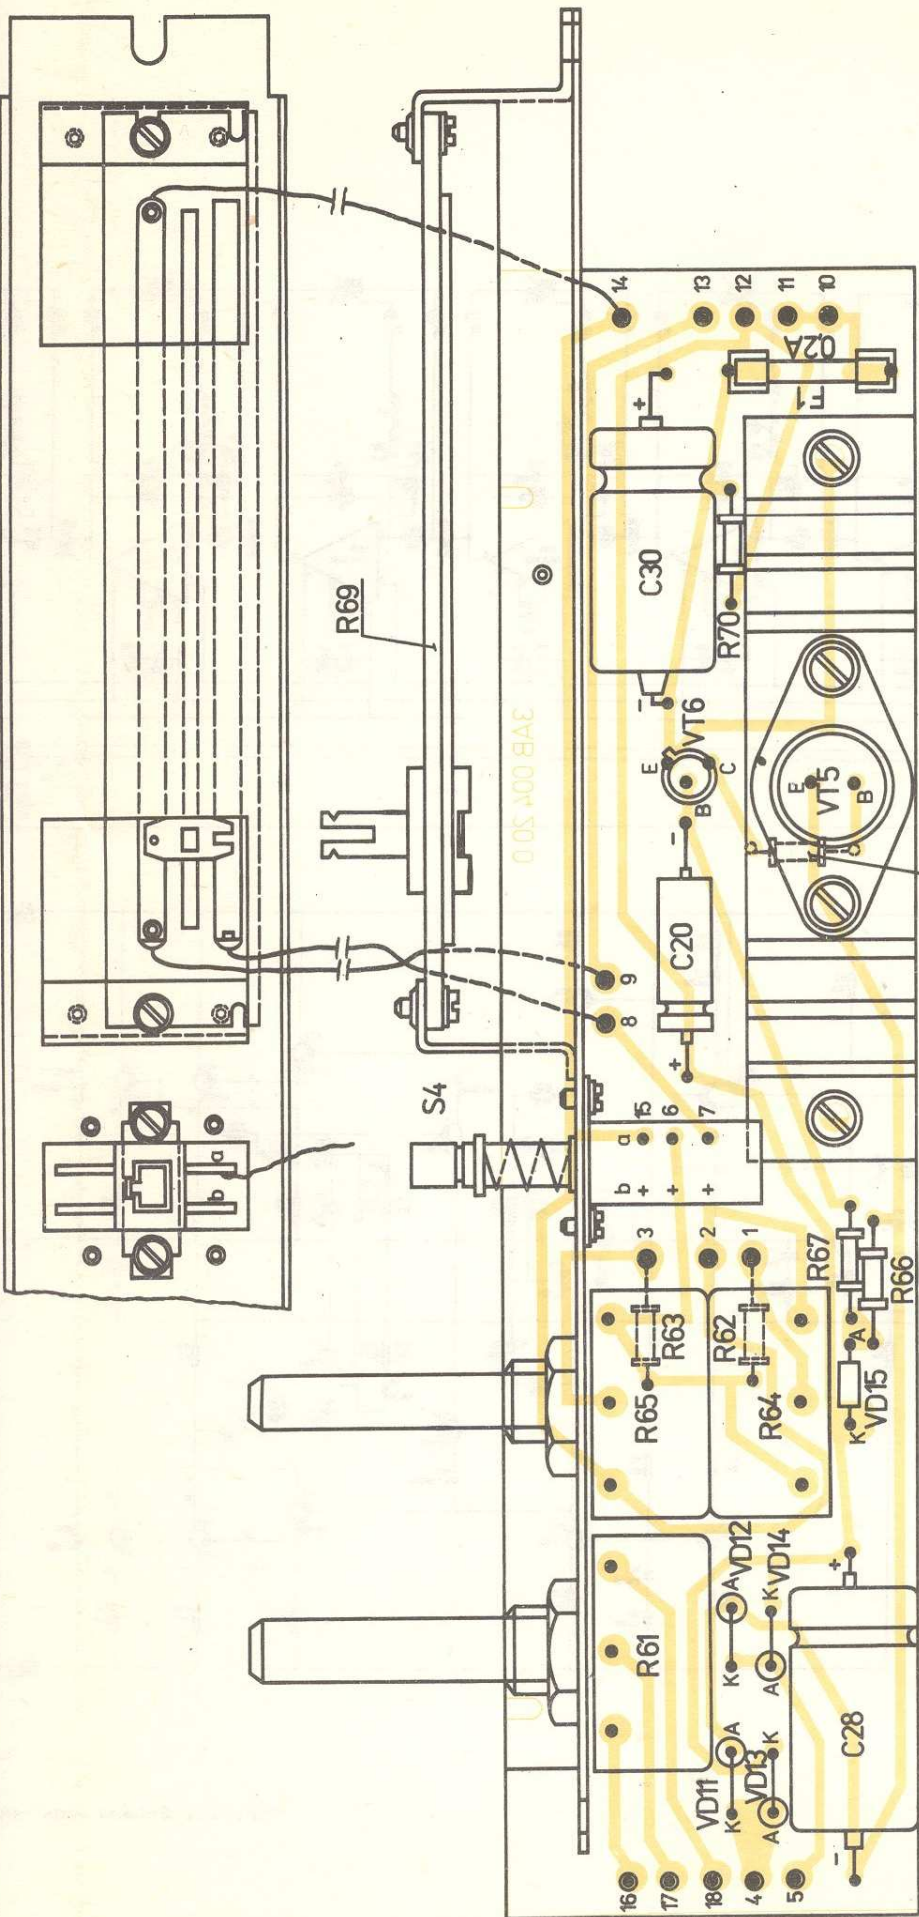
Deska snímání 3AK 052 93 - strana spojů
